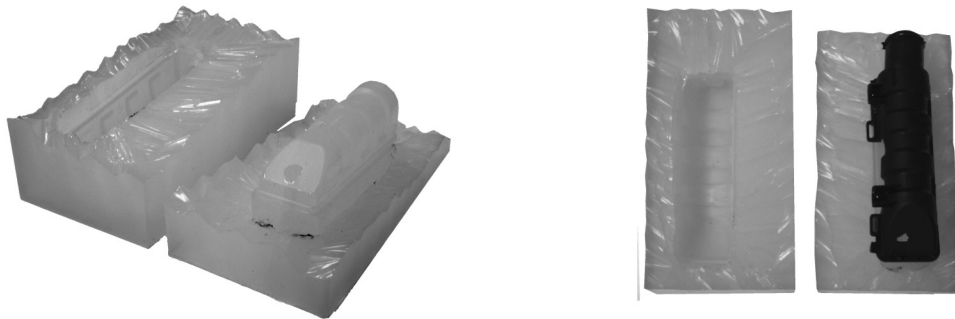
Molde de silicona (izquierda) y molde con el prototipo (derecha)
